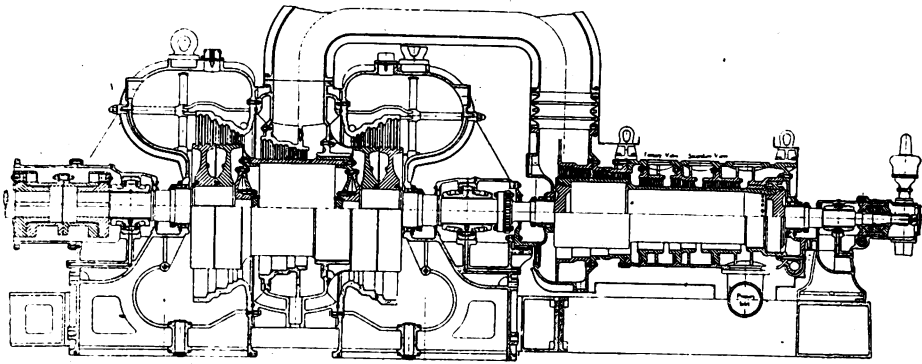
Coupe transversale de la turbine du groupe de 35 000 kw de la Westinghouse Co installé à North West Station à Chicago.
